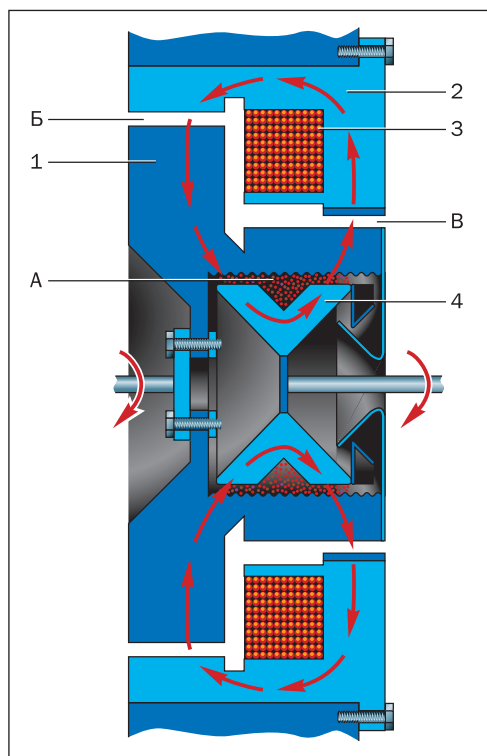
Электромагнитное порошковое сцепление: А, Б, В — зазоры; 1 — ведущая часть; 2 — неподвижный корпус; 3 — обмотка возбуждения; 4 — ведомая часть
